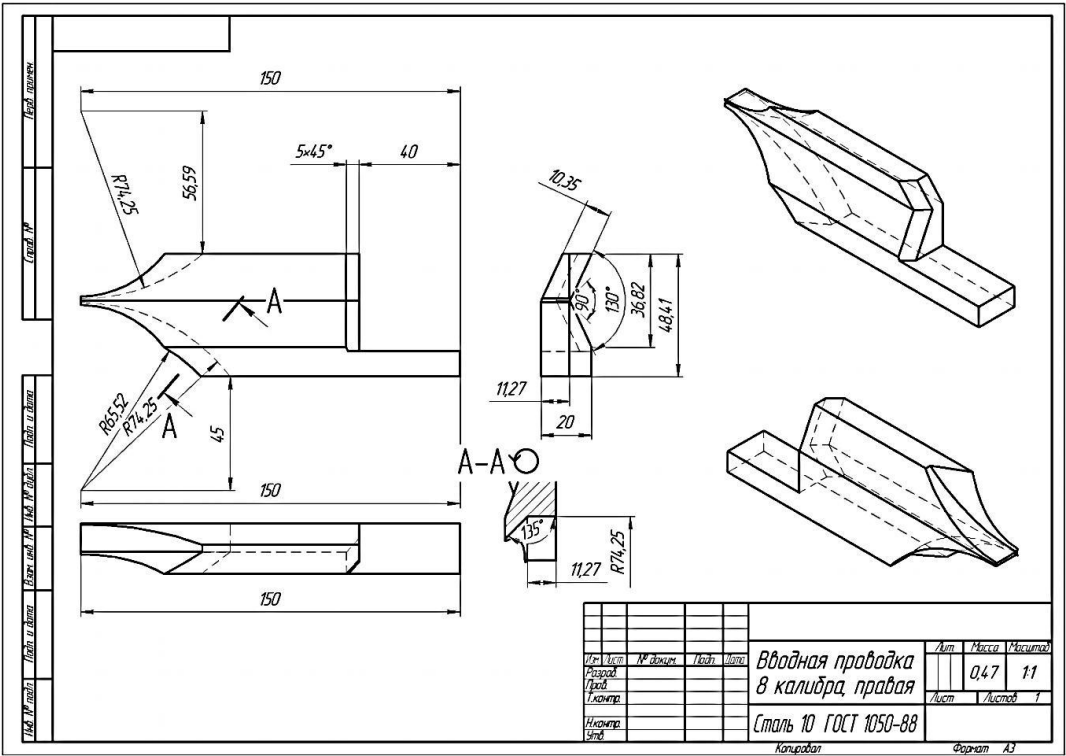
Рабочий чертеж элемента проводковой арматуры для 8 калибра рабочих валков
